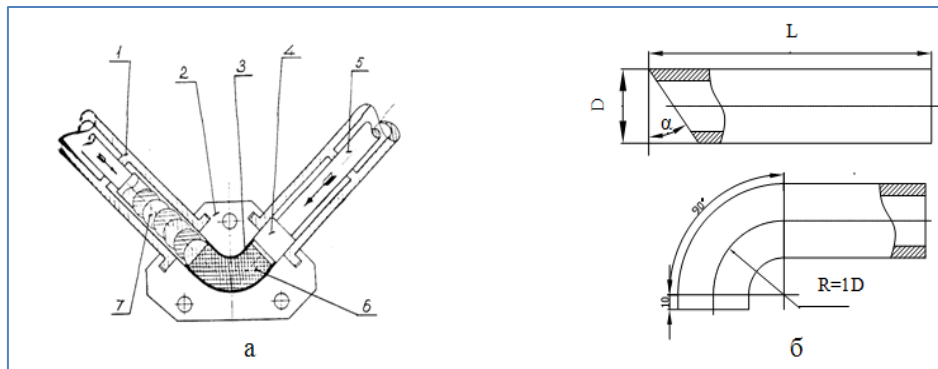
а) схема процесса формообразования крутоизогнутого патрубка: 1 – гидроцилиндр, 2 – матрица фильера, 3 – заготовка, 4 – пуансон, 5 – шток, 6 – эластичный наполнитель, 7 – шариковая опавка; б) конструкция заготовки и крутоизогнутого патрубка
